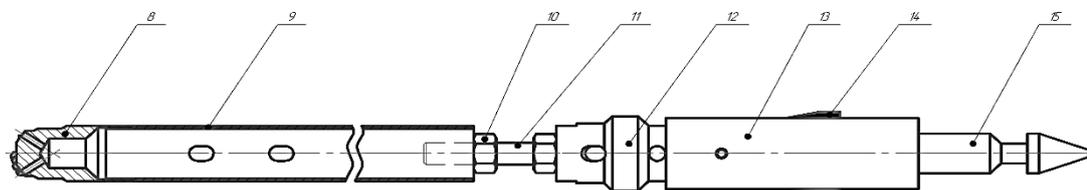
Внутренняя бурильная труба с BIT PDC- 45,5. 8-внутреннее долото BIT PDC -45,5 мм; 9-внутренняя бурильная труба д-56 мм; 10-регулирующая гайка; 11-шпindelь; 12-корпус нижней защелки; 13- корпус защелки втягивающего; 14-стопорные защелки; 15-гребковый (копьевидный) механизм для сцепления овершота.
